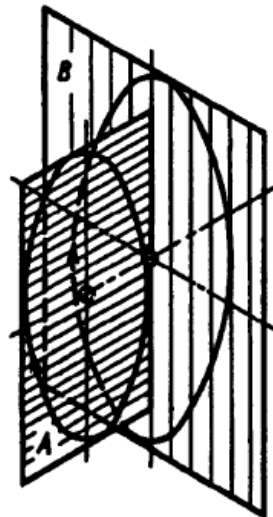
Схема фрезерування тіл обертання торцевими фрезами
